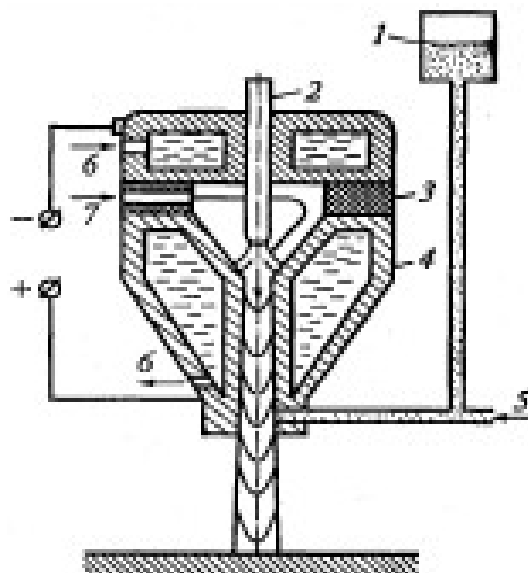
Схема процесу плазмового напилювання: 1 - порошковий дозатор; 2 - катод; 3 - ізоляційна прокладка; 4 - анод; 5 - транспортуєчий газ; 6 - холодна рідина; 7 - плазмоутворений газ
